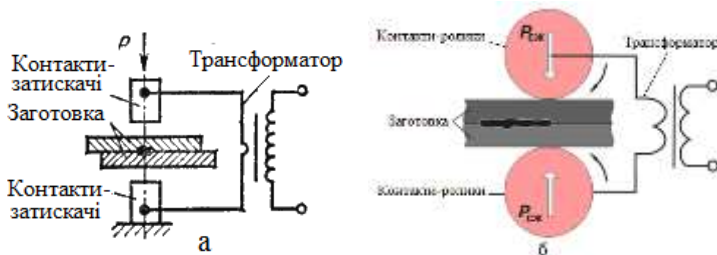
Схема точкового (а) та шовного (б) зварювання
